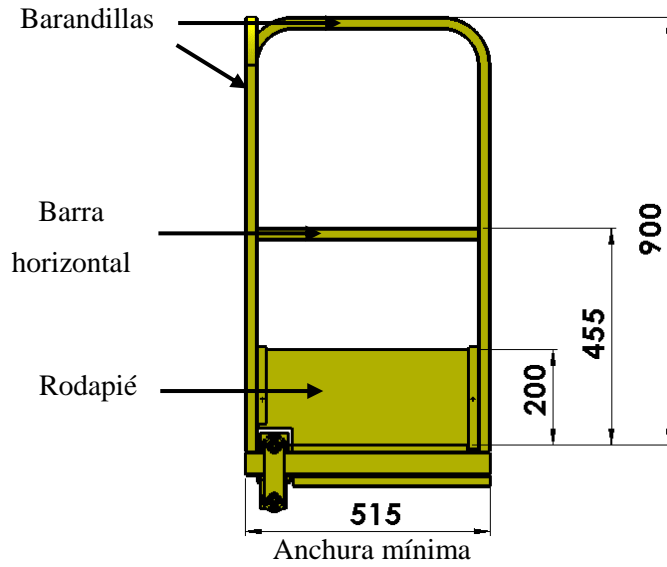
Canasta de elevación constituida por barandillas, barras horizontales y rodapiés.
